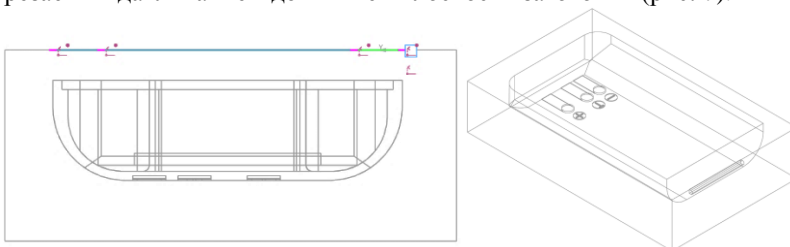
Спроецированный контур заготовки и вычитание из заготовки
